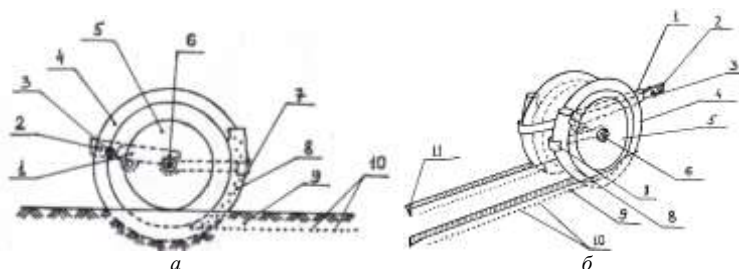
Двухдисковый сошник с односторонними ребордами-бороздообразователями: а – вид сбоку; б – трехмерный вид; 1 – корпус сошника; 2 – отверстия; 3 – болты; 4 – диски; 5 – реборды-бороздообразователи; 6 – оси; 7 – пластина; 8 – семянаправитель; 9 – бороздка; 10 – семена; 11 – щель
